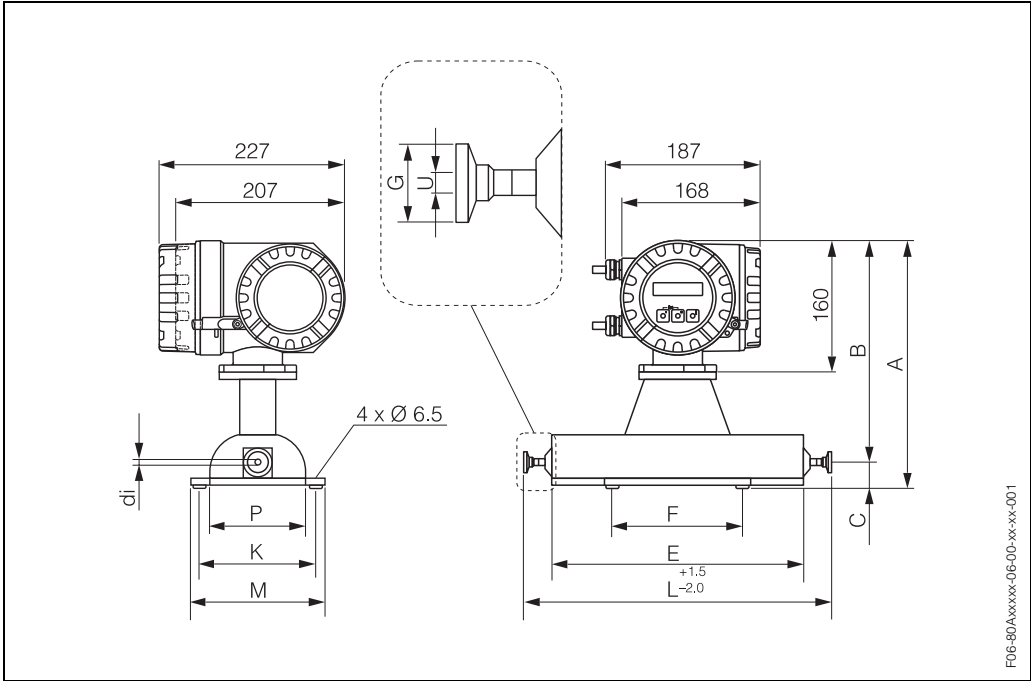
Abmessungen Promass A: 1/2"-Tri-Clamp-Anschluss (angeschweißt)
